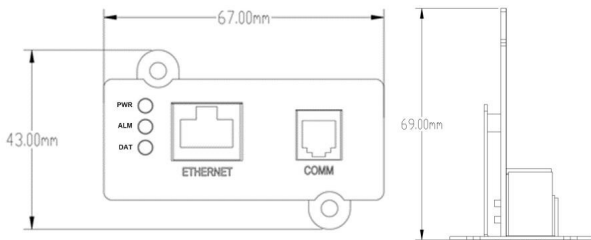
Чертеж конструктивных размеров.
